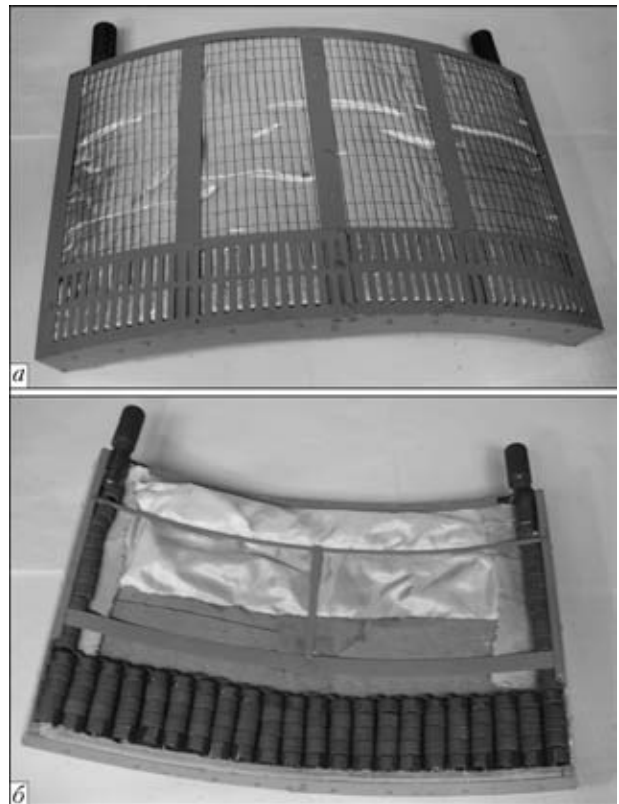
Общий вид базовой конструкции СНС (а) и расположение нагревательного элемента (б)
